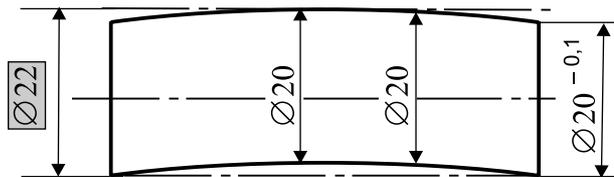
Welle mit nicht eingeschränkter Geradheitsabweichung und möglichem Hüllmaß
